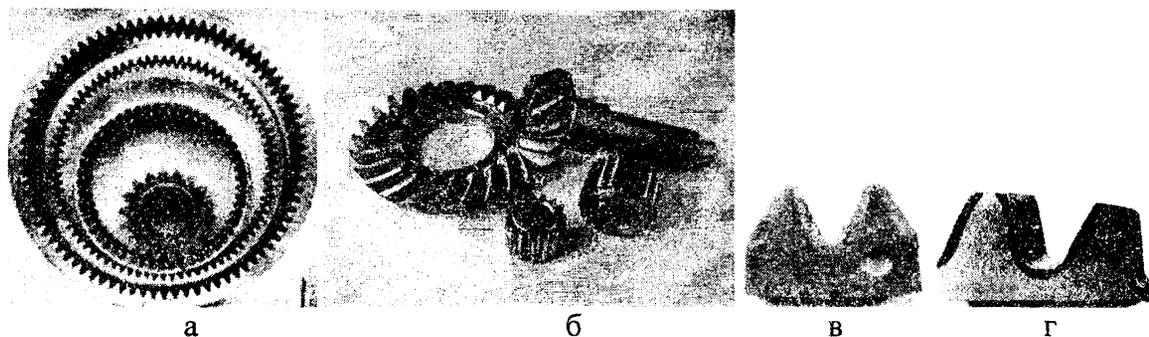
а,б - шестерни колесной и главной передач автомобилей МАЗ и МЗКТ; распределение закаленной зоны в сечении из зубьев после контурной закалки с применением индукционного нагрева: в – ведомой шестерни колесной передачи, г – ведомой шестерни главной передачи заднего моста автомобиля МАЗ.
